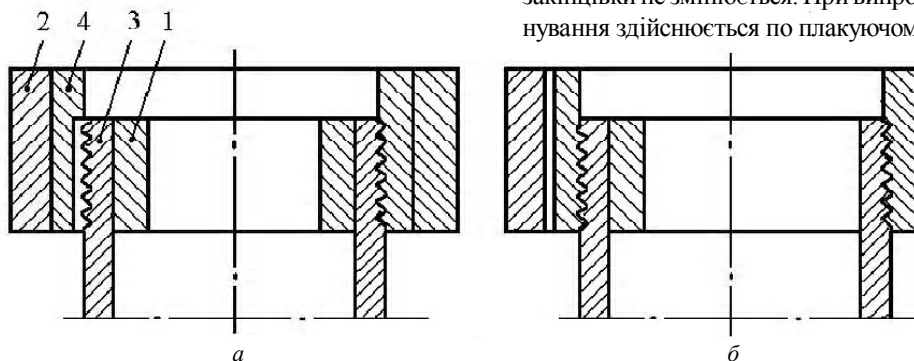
Схема отримання клинопресовим зварюванням з'єднання закінцівки з алюмінієвого сплаву Д20 з циліндричним конусом з КМ боралюміній з поздовжнім і окружним армуванням: а – до зварювання, б – після зварювання
